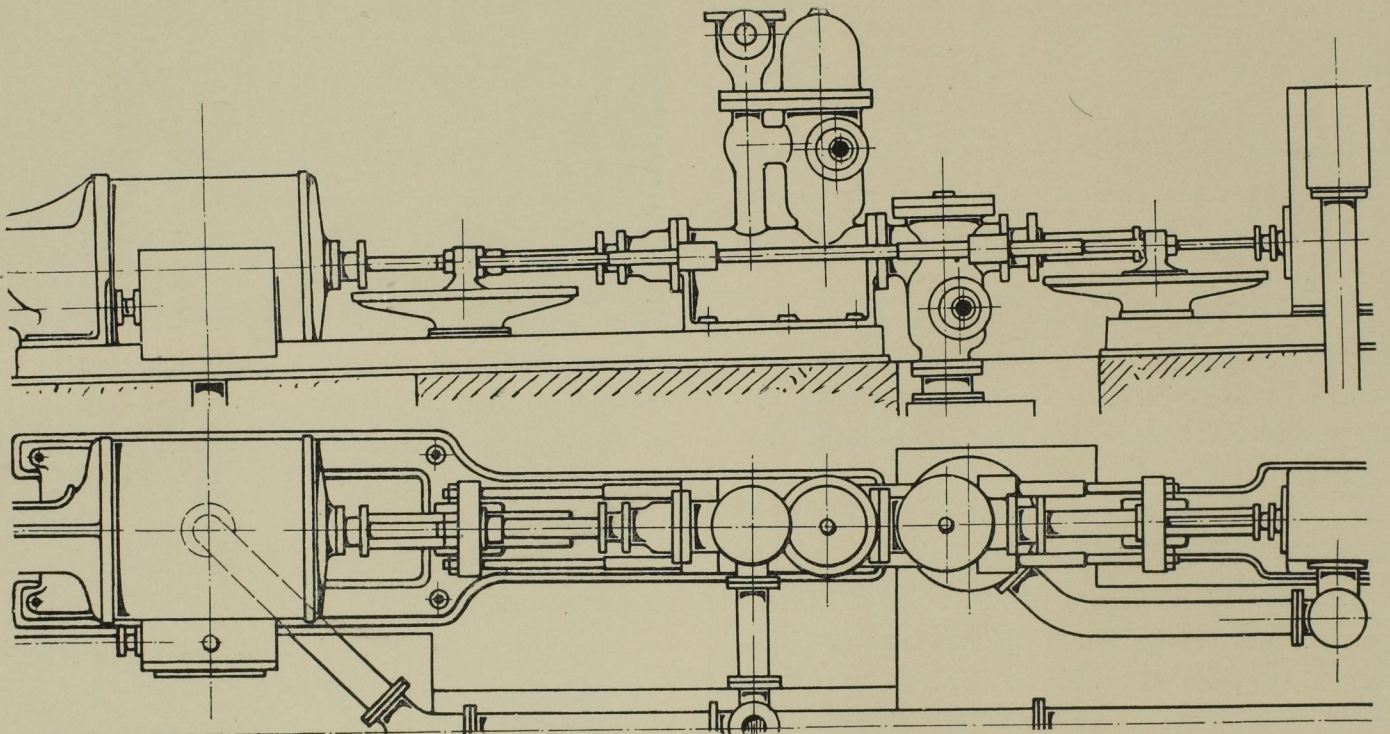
Seitenansicht und Grundriss. Masst. 1:50.
